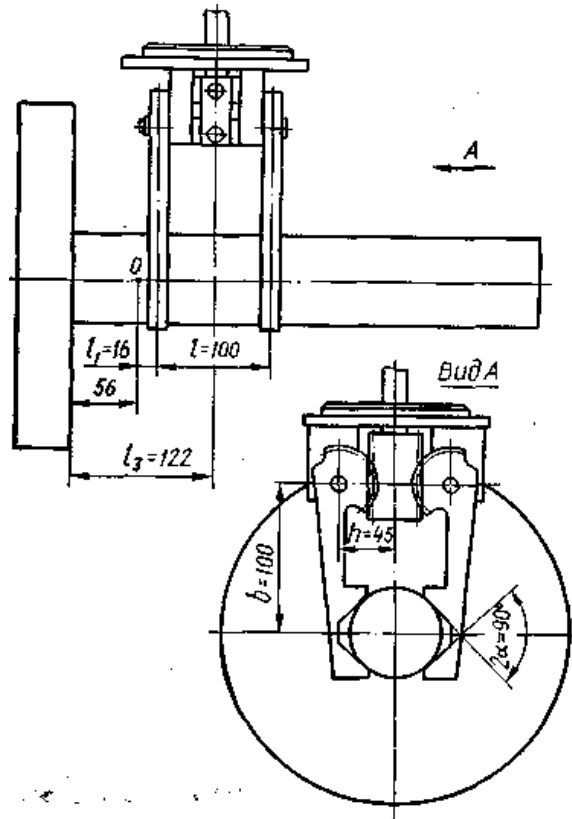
Схема захвату заготівлі двомісного ЗП з рейковим приводом
